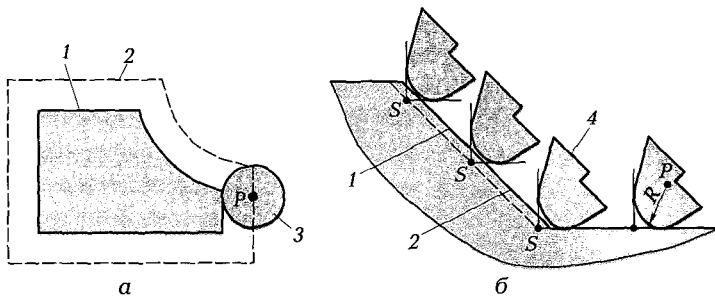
Движение настроечной точки P при фрезеровании (а) и точении (б): 1 — обрабатываемый контур; 2 — движение центра инструмента; 3 — фреза; 4 — резец
